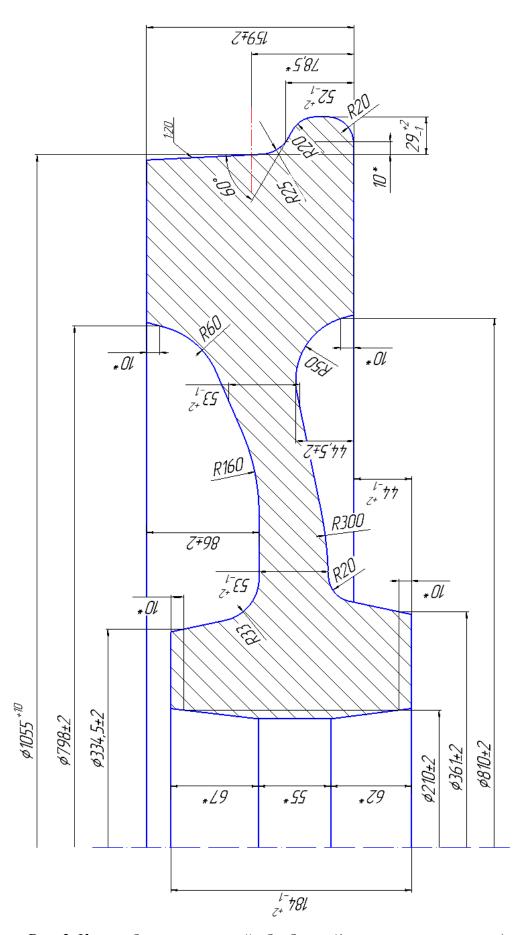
Колесо без механической обработки (* - размеры для справок)
